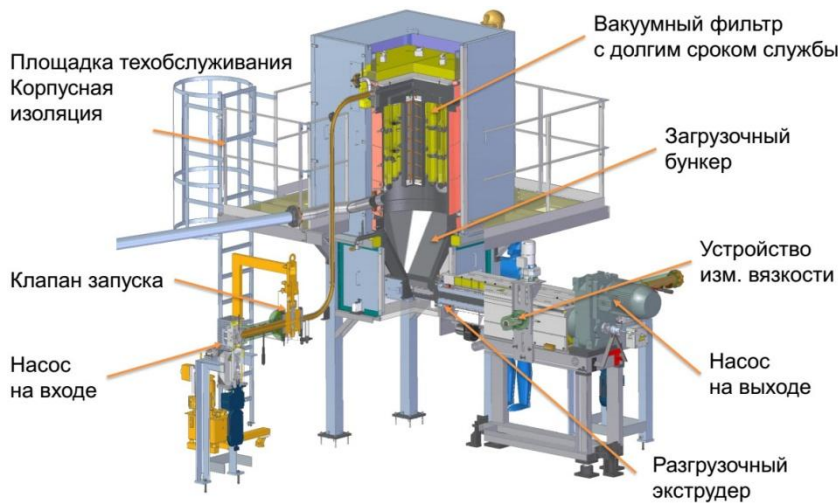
Детали конструкции и основные компоненты VacuFil
